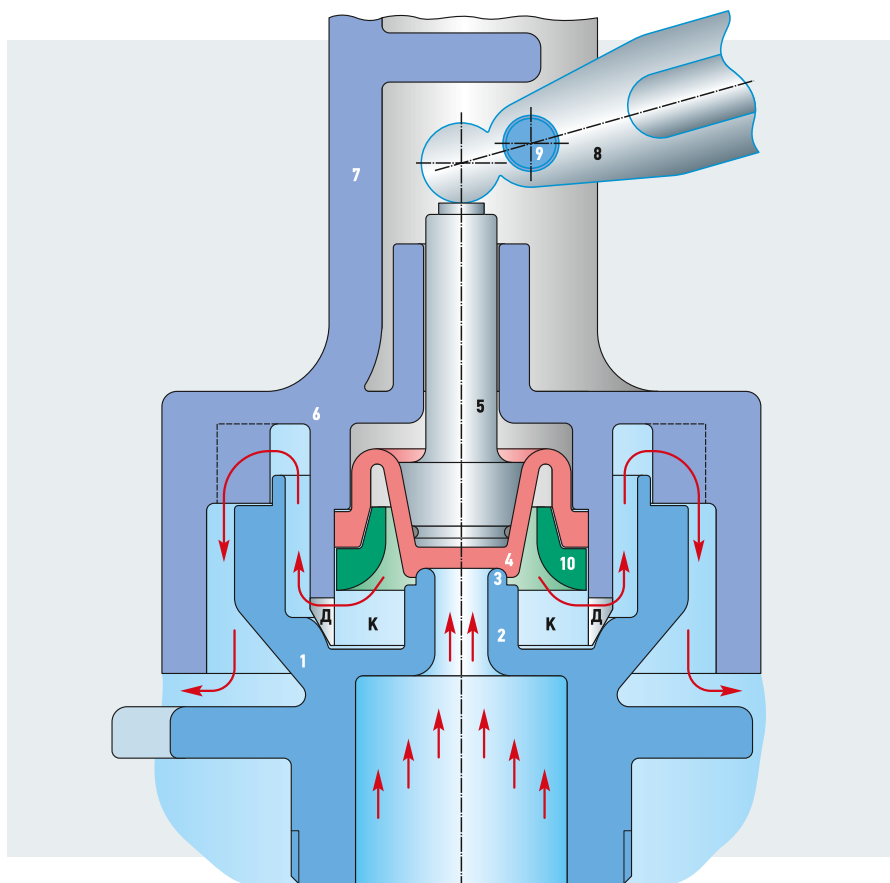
Конструктивная схема узла управления запорно-регулирующим клапаном наполнительной быстрозакрывающейся арматуры противоаварийного типа [1 — верхняя часть штоца, в которой размещено сопло 2 с торообразным седлом 3; 4 — эластичный клапан с диафрагмой чулочного типа; 5 — толкатель клапана 6 — крышка запорного устройства с вертикальной стойкой 7; 8 — рычаг (нижнее плечо параллелограммного механизма); 9 — ось поворота рычага 8; 10 — стопорное кольцо, установленное по плотной посадке; Д — две дросселирующие поток воды щели, К — рабочая камера клапанной системы]
